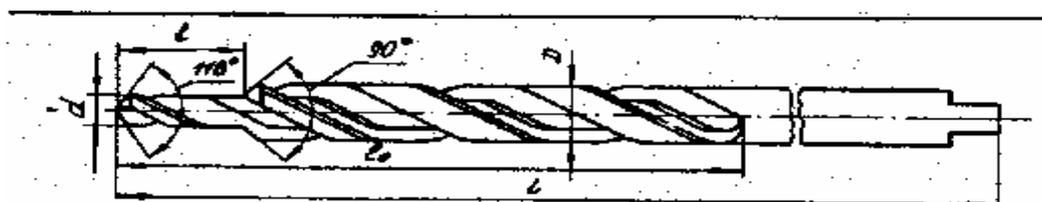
Сверла ступенчатые для одновременного снятия фаски и сверления под резьбу по ОСТ 2И21-1-76
